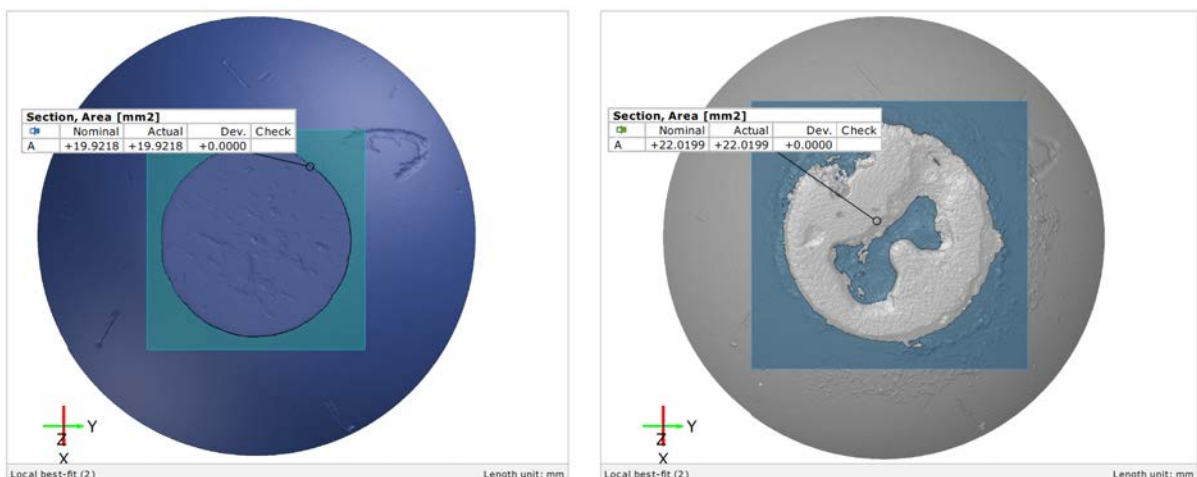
Měření změny axiální délky elektrody v GOM Inspect.
